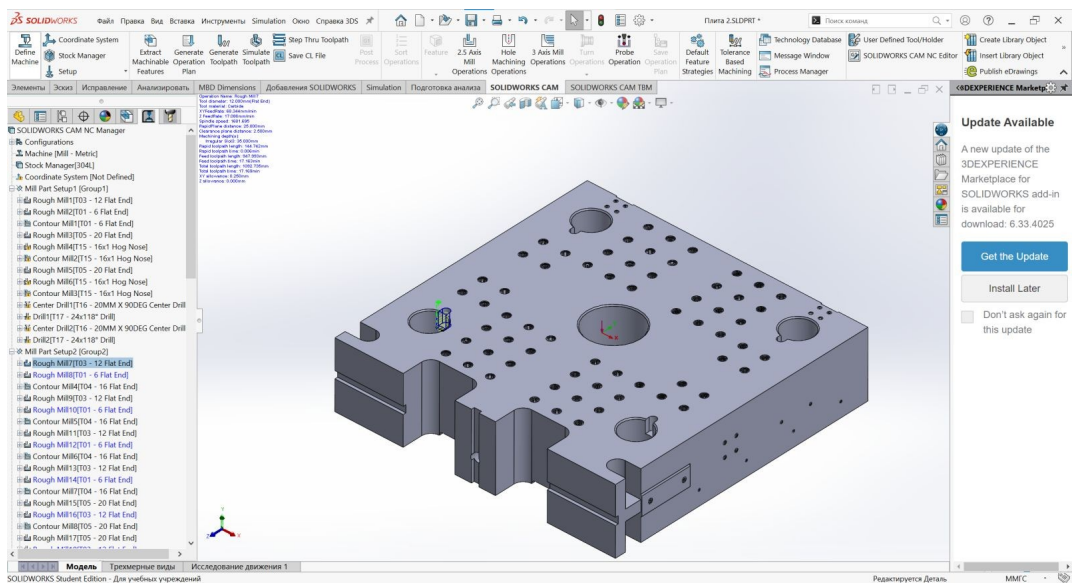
Траекторія руху інструменту при фрезеруванні паза
